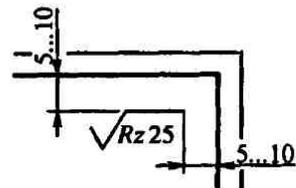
Обозначение одинаковой шероховатости для всех поверхностей
